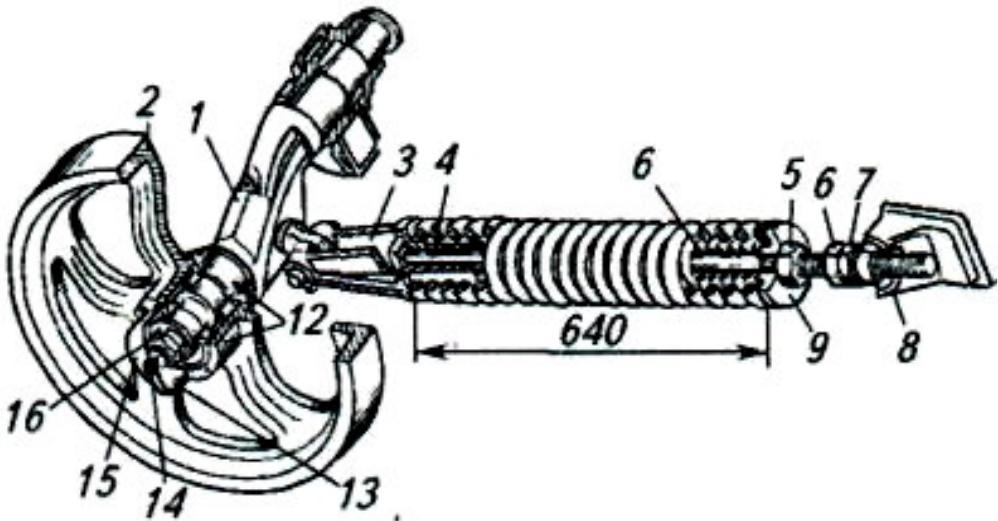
Натяжное устройство трактора с балансирующей подвеской
